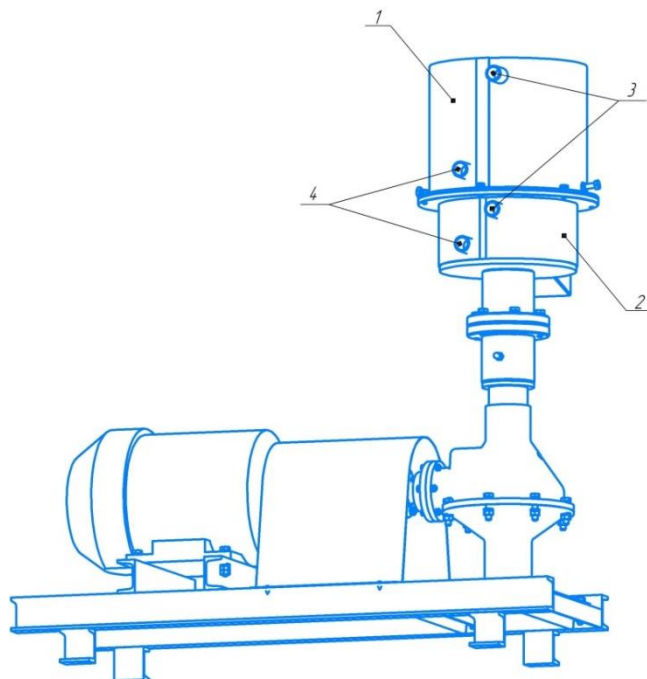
1 – рубашка загрузочного бункера, 2 – рубашка корпуса прессующего узла, 3 – патрубки подачи охлаждающей жидкости, 4 – патрубки обратного движения охлаждающей жидкости.
